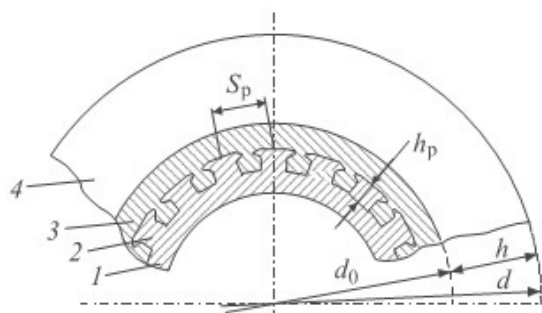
Биметаллическая труба с обжатыми вершинами рельефов на несущей трубе [23]:
